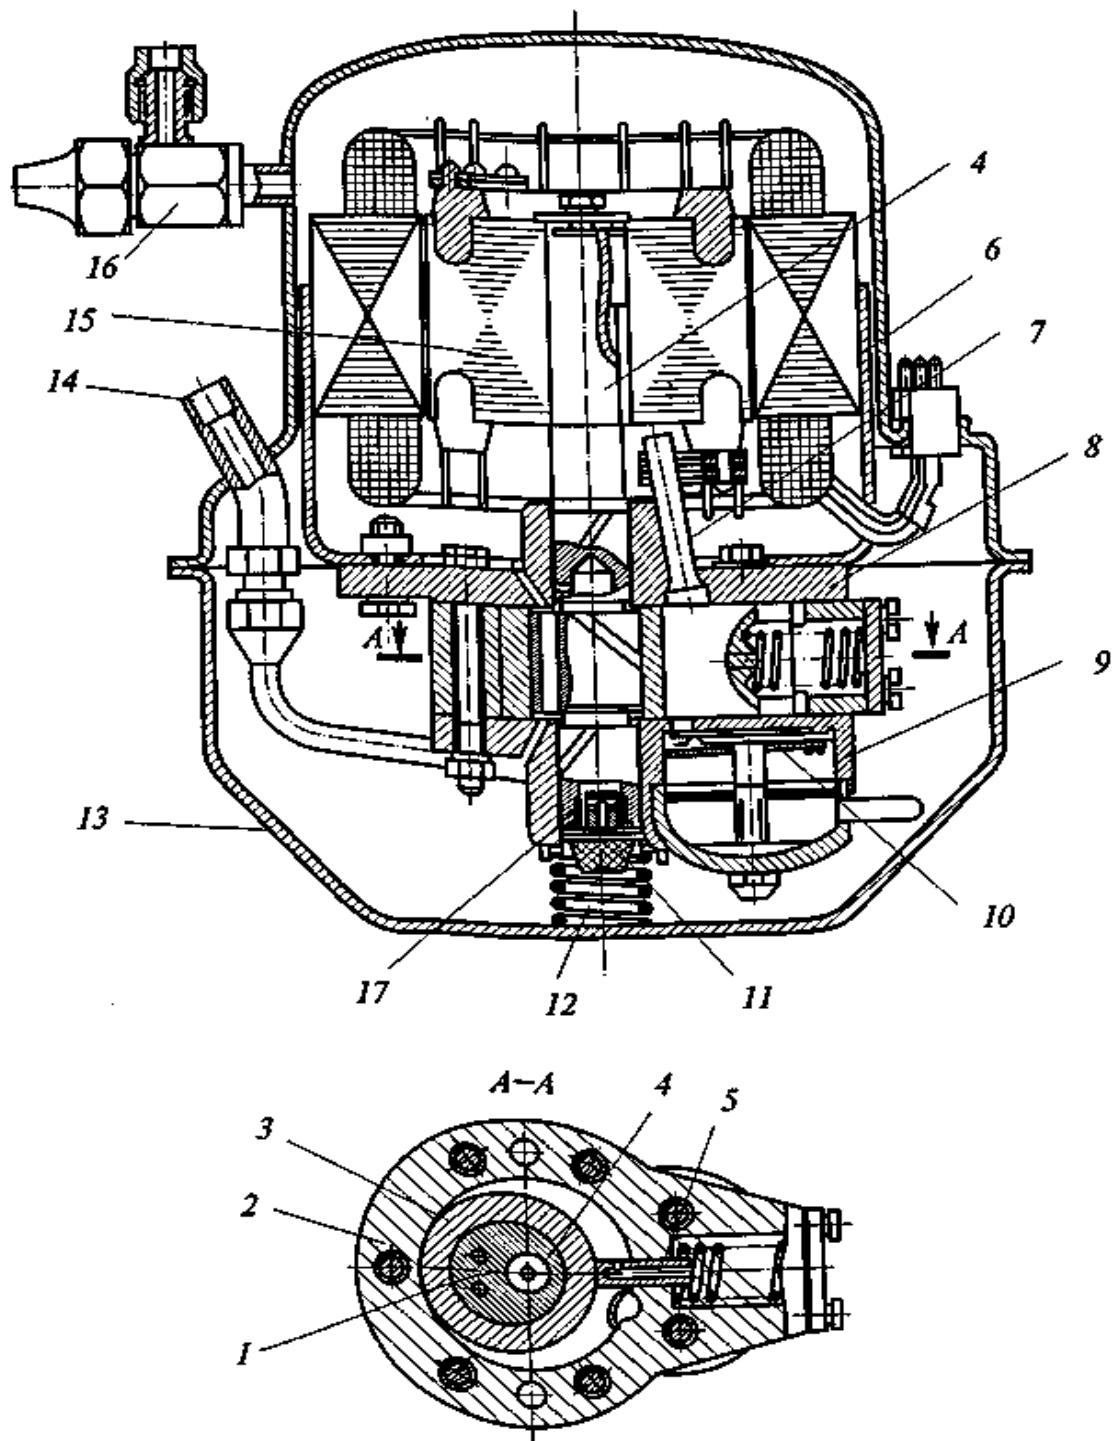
Герметичный компрессор с катящимся ротором типа ФГр:
